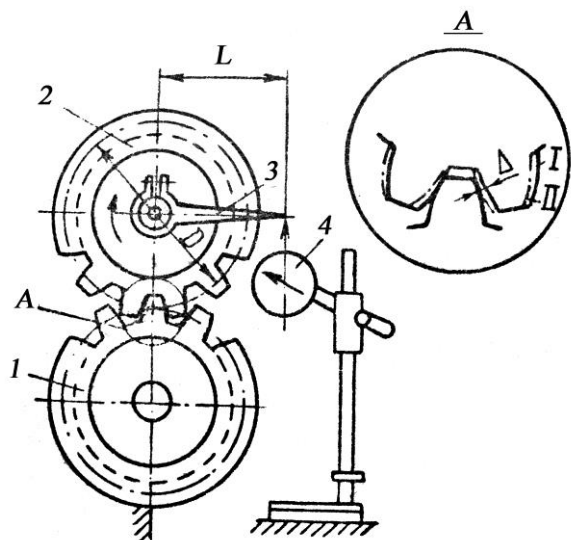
Контроль бокового зазору в зачепленні циліндричних зубчастих коліс: 1 — нижня шестірня; 2 — зубчасте колесо; 3 — хомут; 4 — індикатор; I—II—положення, зубчастого колеса
